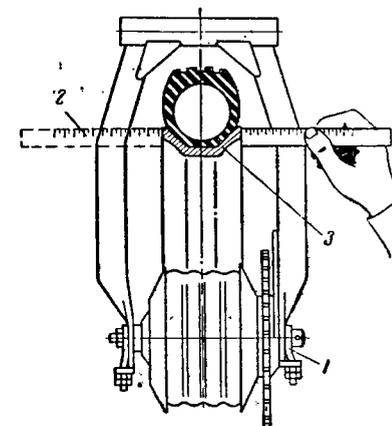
Проверка правильности установки заднего колеса: 1 — серга натяжения цепи; 2 — линейка; 3 — обод колеса.
